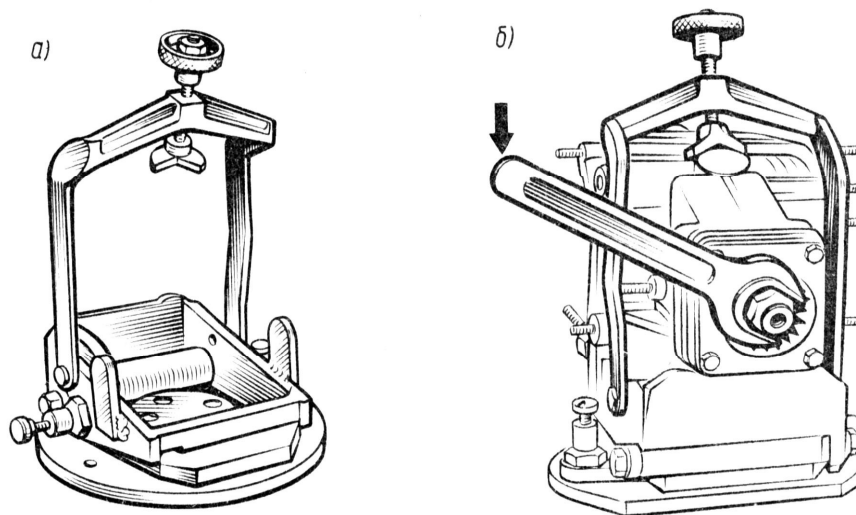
приспособление для разборки и сборки редуктора заднего моста: а) – приспособление; б) – установка редуктора заднего моста на приспособление.
